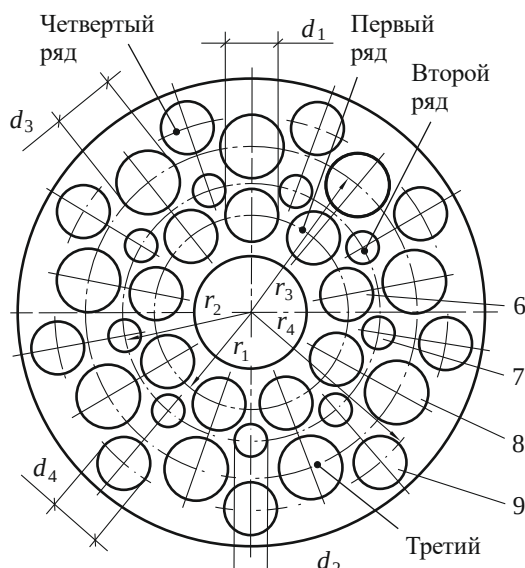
Вид на торец четырехрядного блока цилиндров аксиально-поршневой гидромашины
